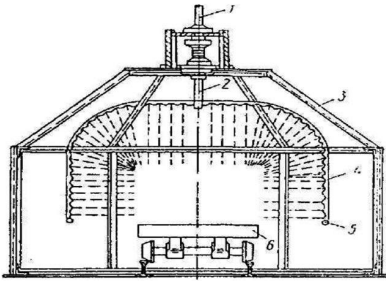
Однокамерна установка для очищення: 1 – підвідний патрубок; 2 – приєднувальний штуцер; 4 – перфорована труба; 5 – насадка; 6 – візок
